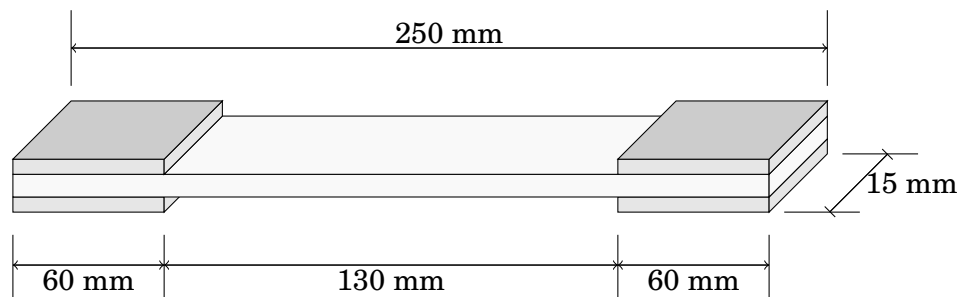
Géométrie et dimensions des éprouvettes testées exprimées en mm
